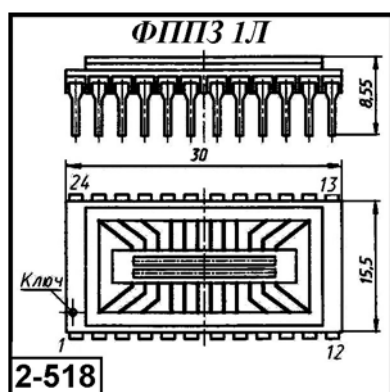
Внешний вид и габаритные размеры ФППЗ 1Л
